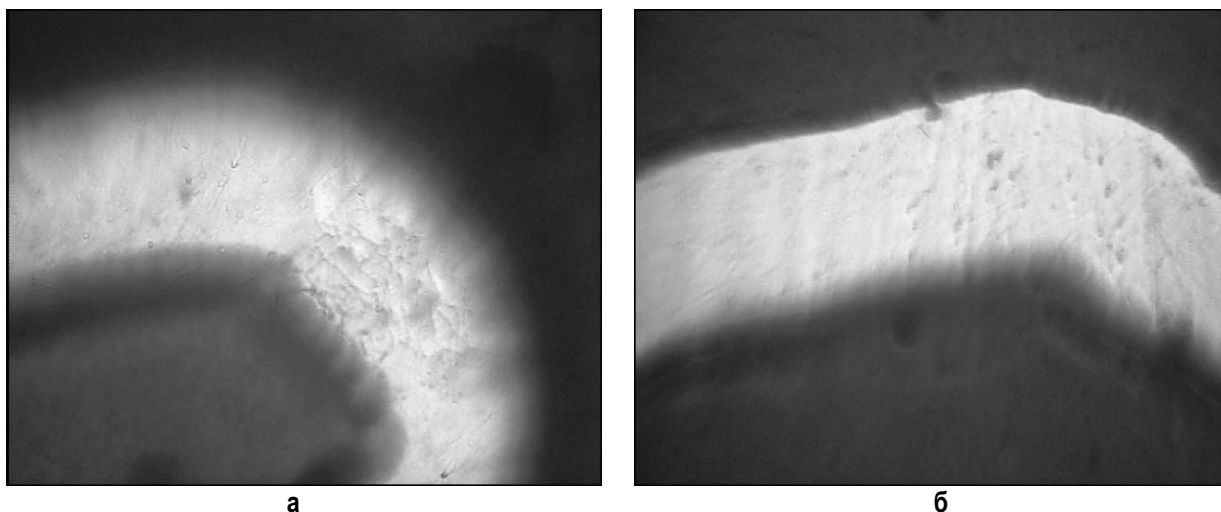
Внешний вид сварного соединения образцов цепочек, полученных с применением различных режимов сварки (а – образец 7; б – образец 11),  $\times 120$
